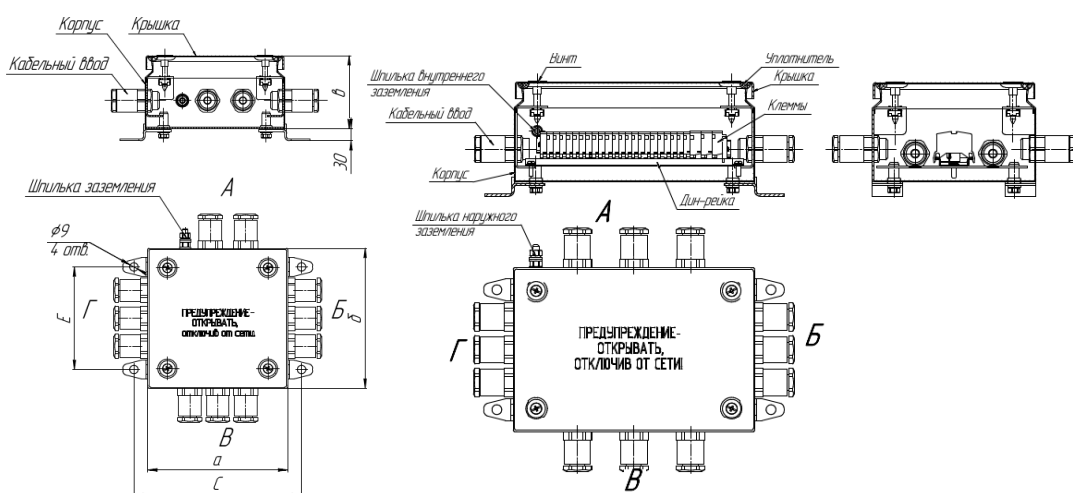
Общий вид, габаритные и присоединительные размеры коробок ЕхКК-С, ЕхКК-Н
